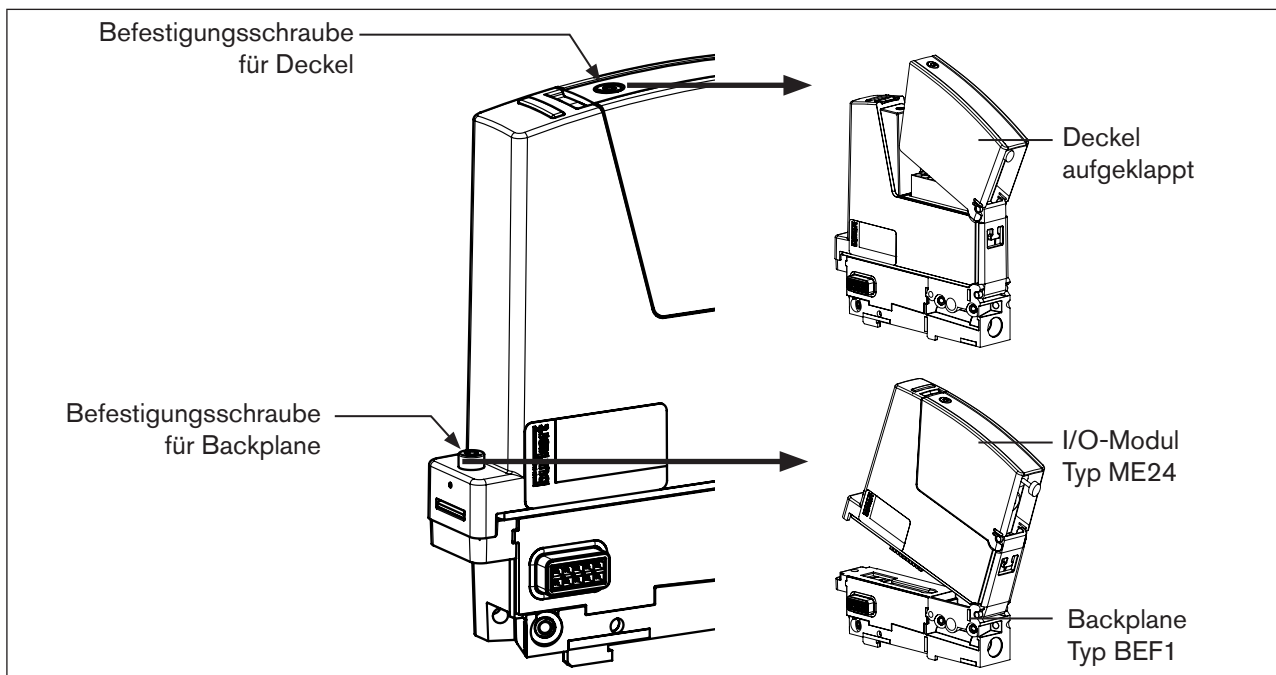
Gerätetausch, I/O-Modul Typ ME24
